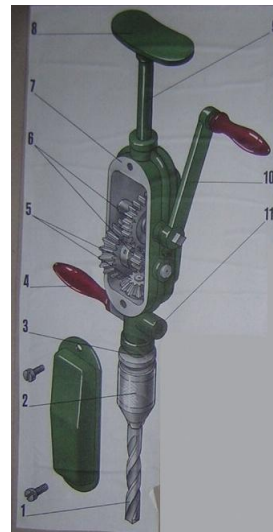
Ручний дріль. Будова та кінематична схема: 1 – свердло; 2 – патрон; 3 – шпиндель; 4 – упорна ручка; 5 – конічна зубчата передача; 6 – циліндрична зубчата передача; 7 – корпус; 8 – упор; 9 – стержень; 10 – ручка приводу; 11 – отвір для кріплення упорної ручки
